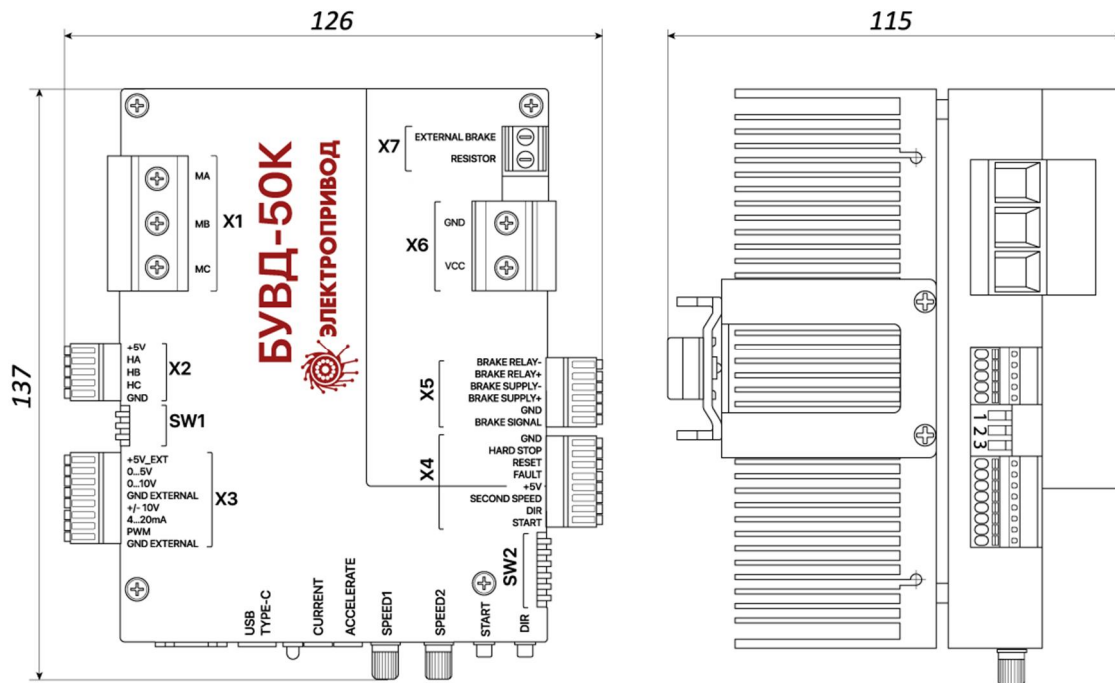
Габаритные и присоединительные размеры блока БУВД-50К
